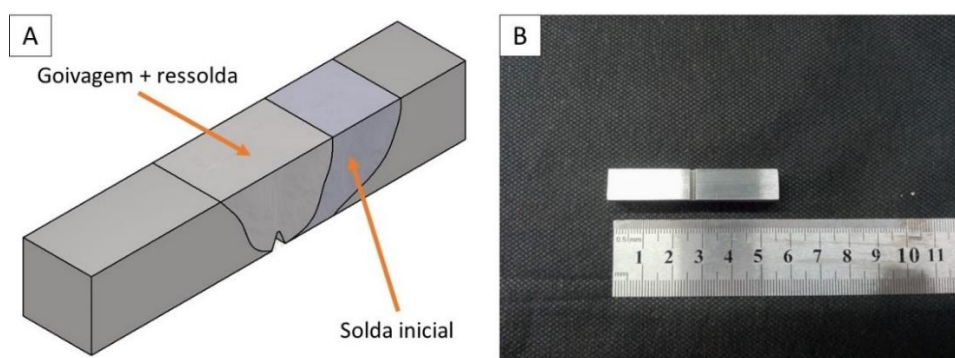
Corpos de provas utilizados para o ensaio de impacto, (a) Detalhe da região com solda inicial e a região goivada e ressoldada alocada na área útil e (b) corpos de prova da amostra goivada e ressoldada usinadas em centro de usinagem
